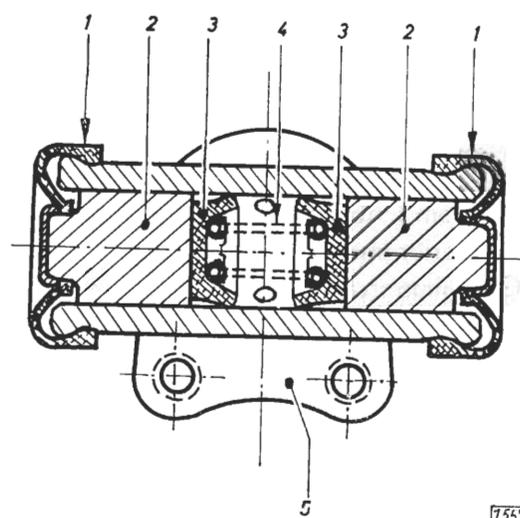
Zweiseitig wirkender Bremszylinder für Hinterradbremse
